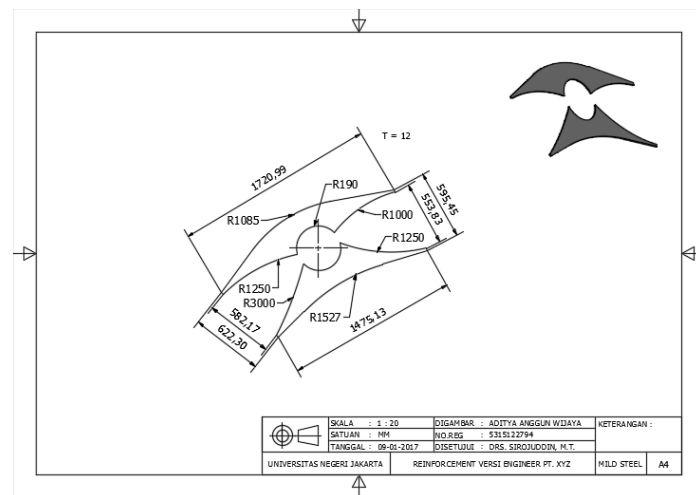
Gambar Dimensi *Part Reinforcement 1 Boom Excavator* Kelas 20 Ton Versi *Engineer* PT. PQR
